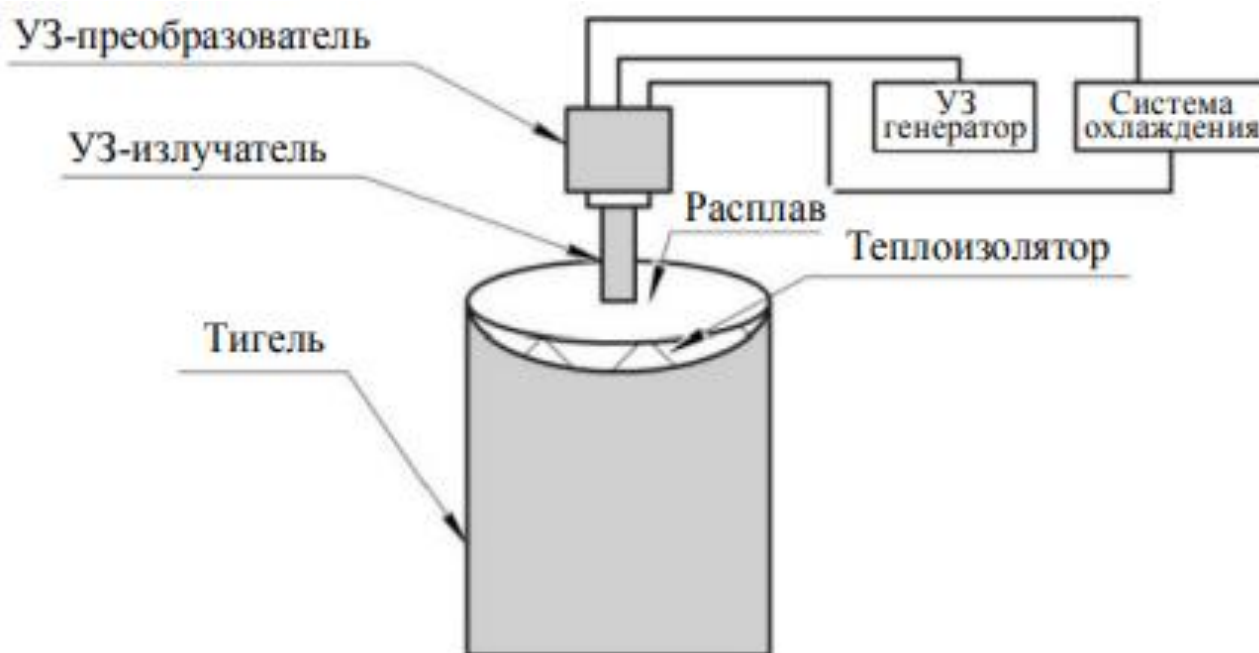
Схема установки для ультразвукової обробки [58]
